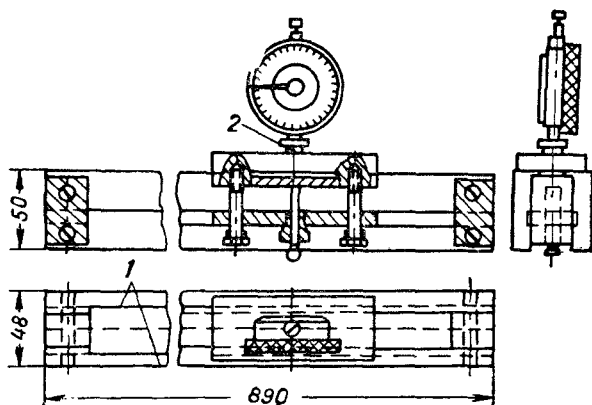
Приспособление для проверки плоскости привалочных поверхностей блоков цилиндров и их головок
